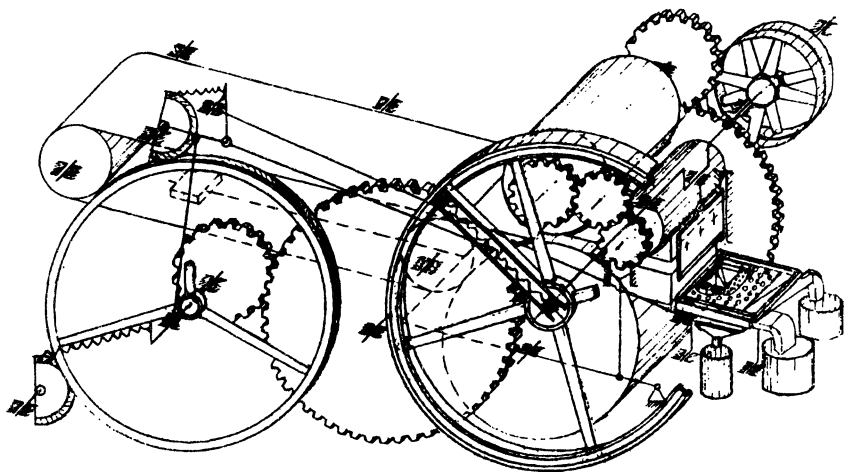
Станок Сан-Гали. Кинематическая схема модернизированного станка для резки трубки.
